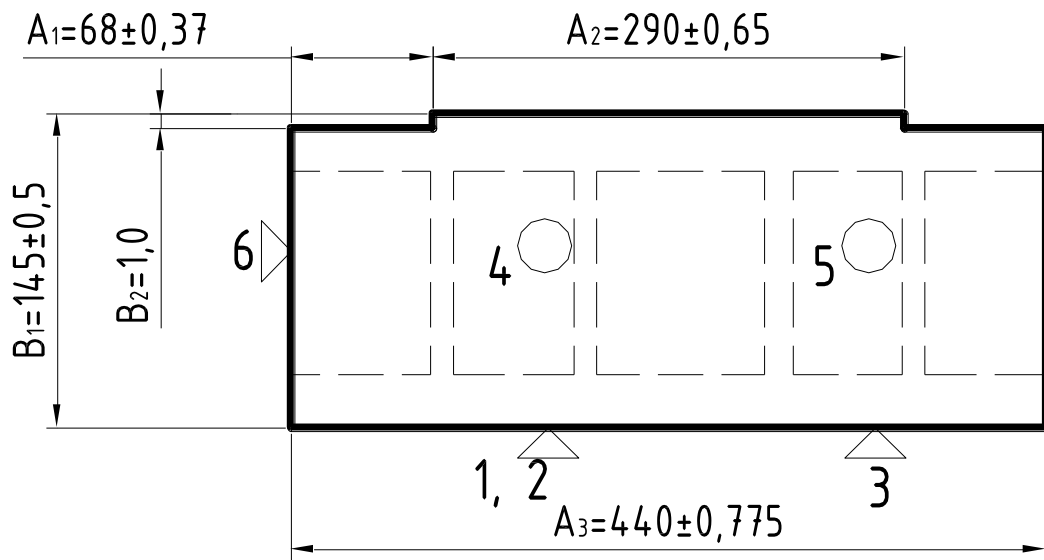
Схема базування при обробленні поверхонь 2 і 3
